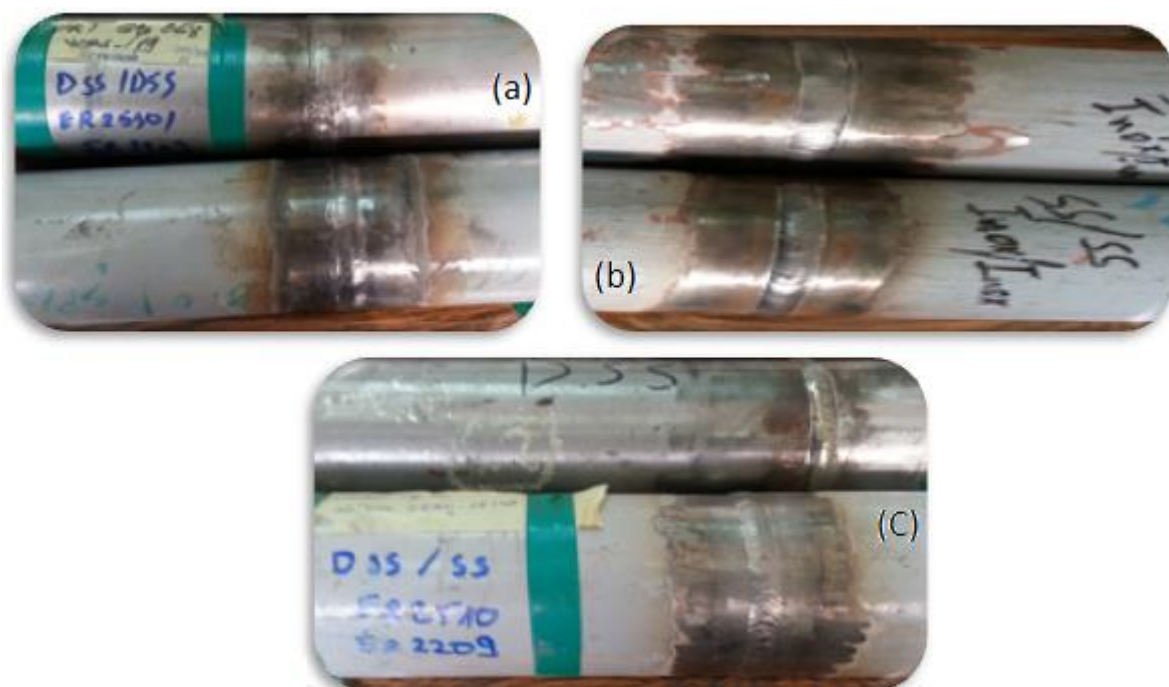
Aspect des cordons de soudures élaborés par TIG : (a)-assemblage AISI 316L/AISI 316L (b)- assemblage Duplex 2205/Diuplex2205 (c) - Assemblage Duplex 2205/AISI 316L
